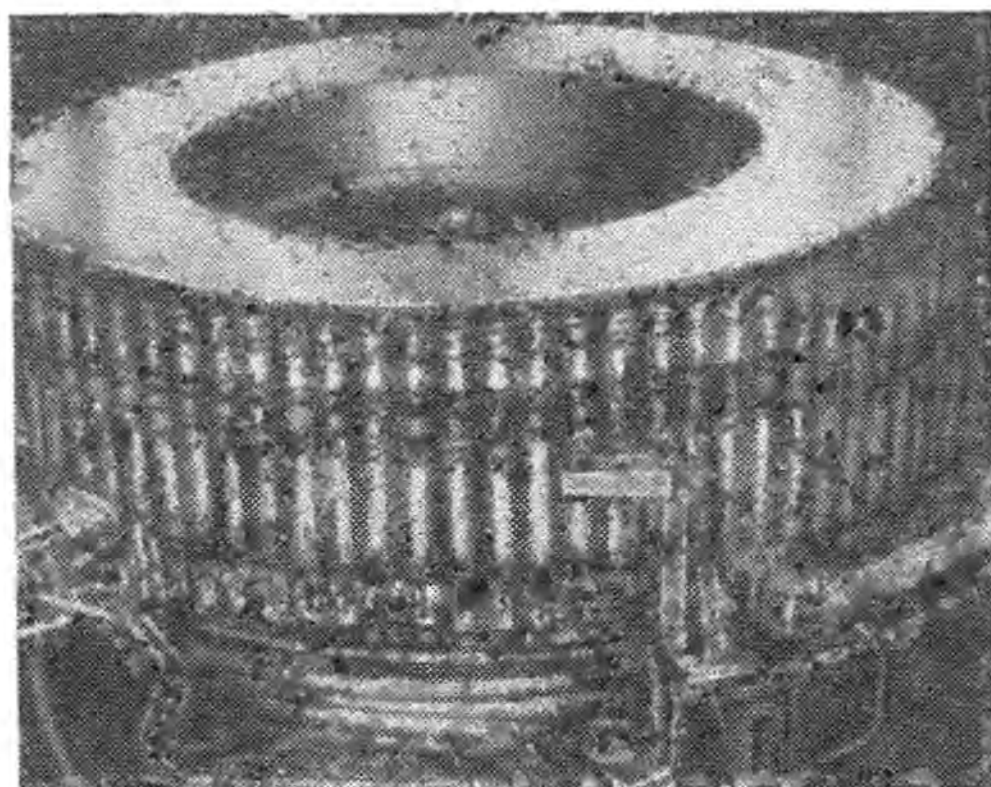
Общий вид роторного полуавтомата для пайки зубков угольных комбайнов
